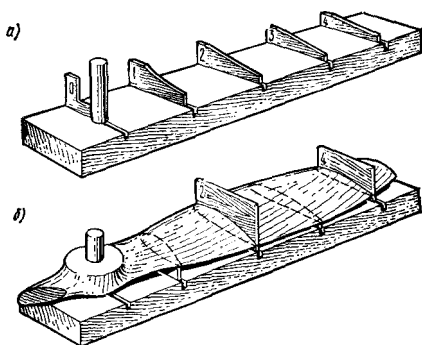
Приспособление для изготовления воздушного винта: а — установка нижнего шаблона; б — установка верхнего шаблона.
